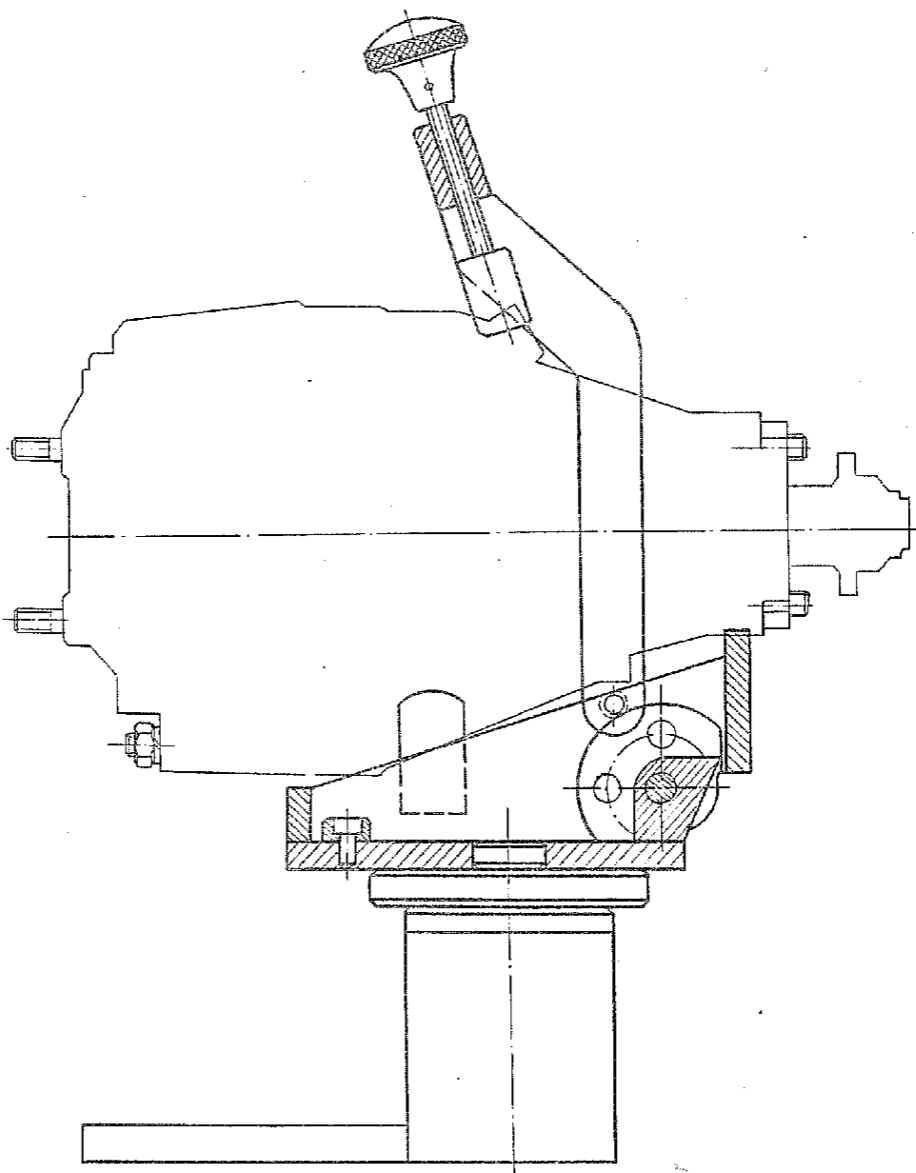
Приспособление для разборки и сборки редуктора заднего моста
